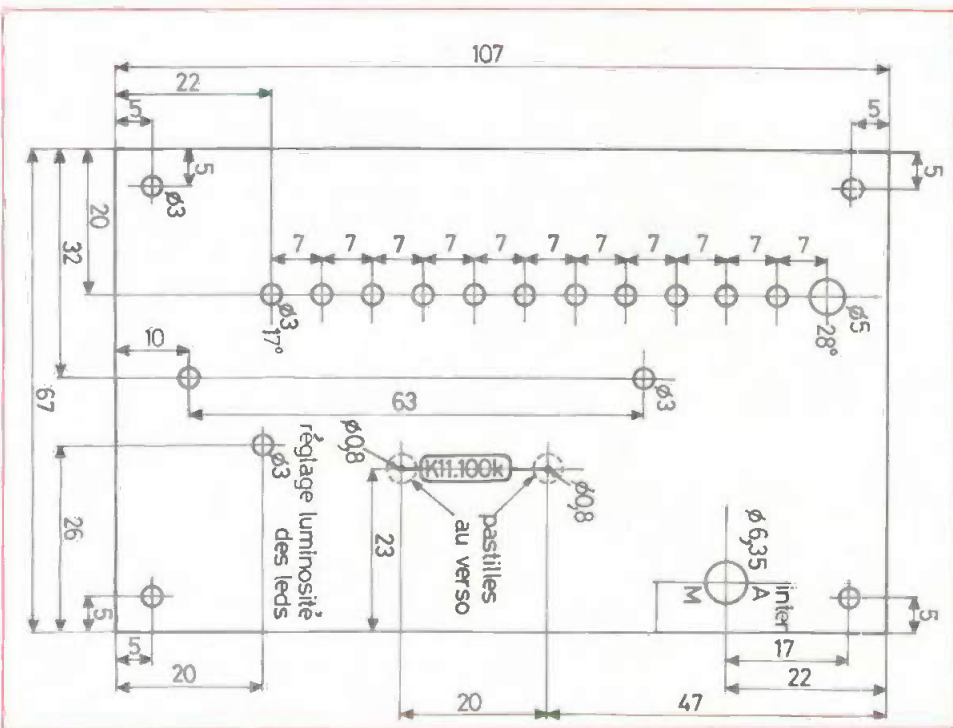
On pourra réaliser en verre époxy une plaque de la dimension d'un couvercle de boîtier P/2.
